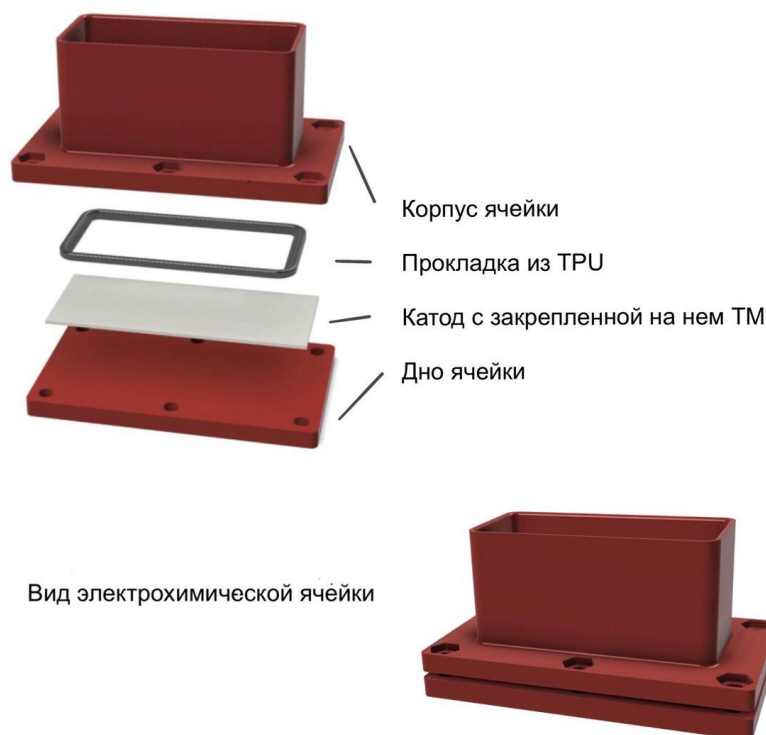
Элементы и вид ячейки для гальванического процесса осаждения металла.
